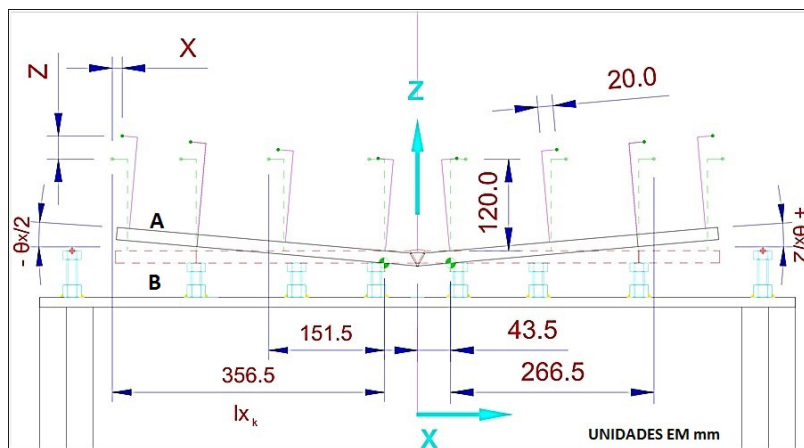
Representação esquemática das distorções de soldagem do corpo-de-prova.
